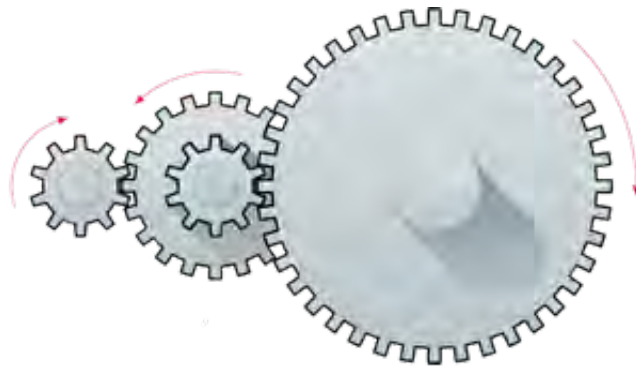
Ejemplo de sistema de reducción por engranaje[17].
